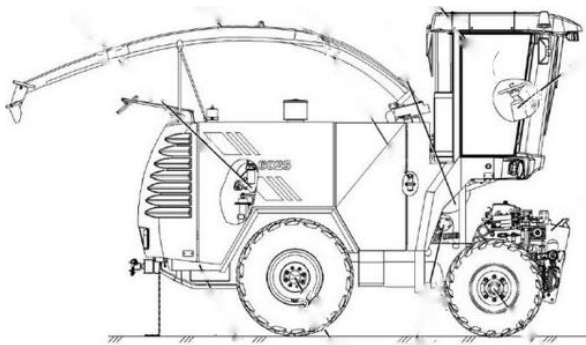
Самоходный кормоуборочный комбайн КВК-6025
